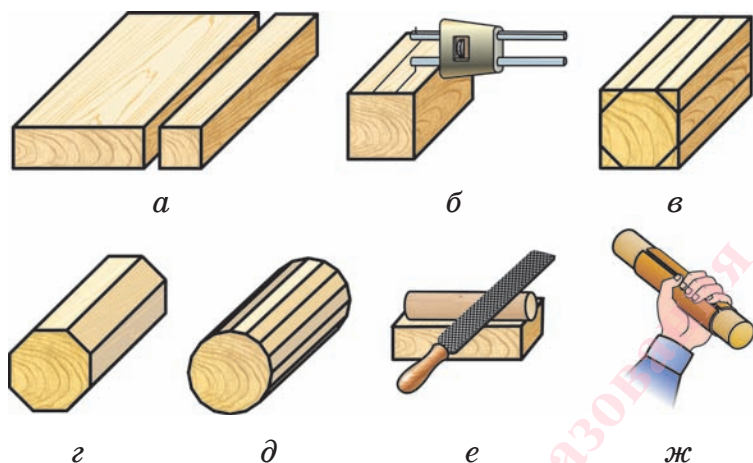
Последовательность изготовления детали с цилиндрической поверхностью:
